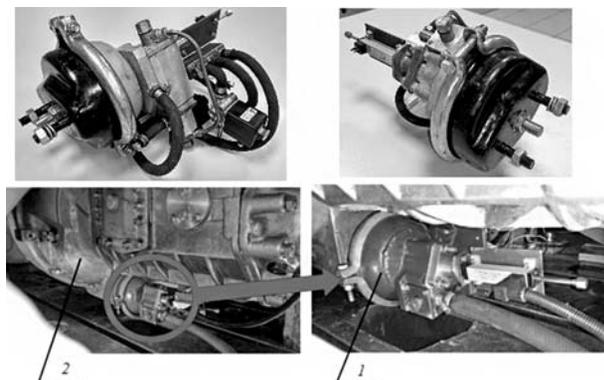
Внешний вид и установка механизма МАУС-16 (поз. 1) на коробке передач TM16-2000 (поз. 2)
